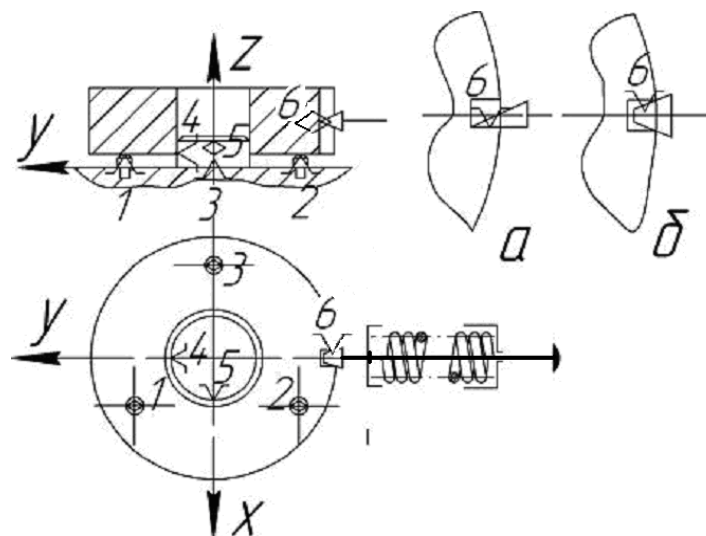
Базування циліндричної заготовки по отвору та торцю з фіксацією повороту навколо центральної осі
